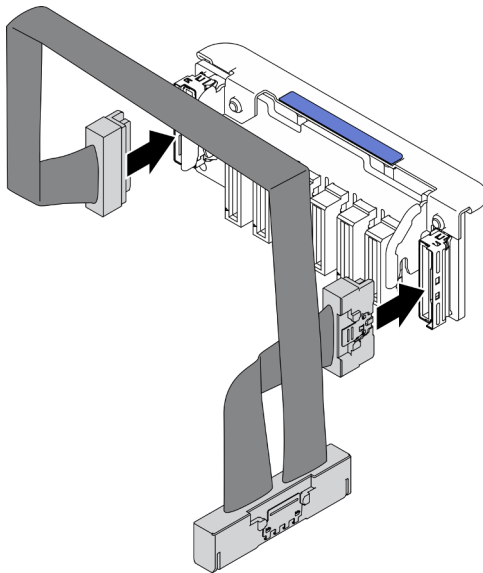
Branchement du câble sur le fond de panier d'unité EDSFF
